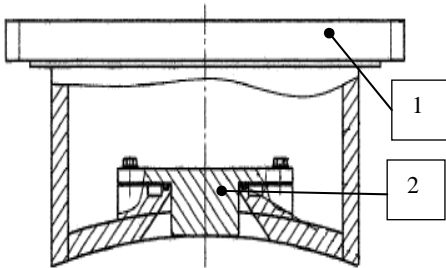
Заглушка II типа 1 – корпус, 2 – заглушка
